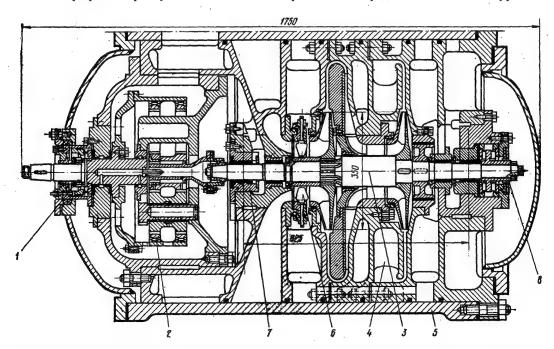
Двухступенчатый фреоновый центробежный компрессор с мультипликатором: 1—уплотнение вала; 2— планетарный мультипликатор; 3— ротор; 4— пакет диафраги; 5— кожух; 6— входной регулирующий аппарат; 7— радиальный подшипник; 8— радиально-упорный подшипник.
